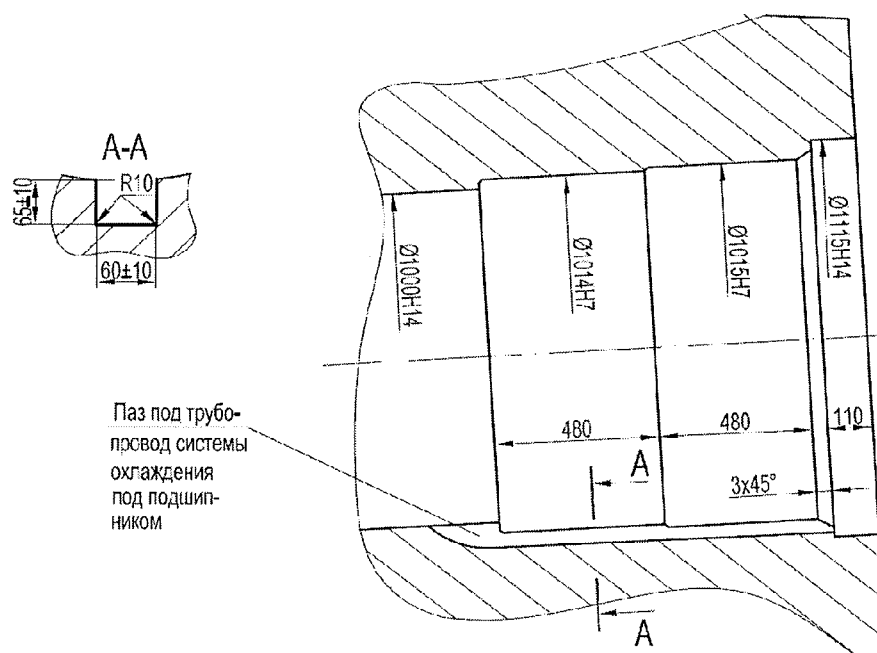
Ориентировочные размеры расточки вварыша переборочного под носовой дейдвудный подшипник
